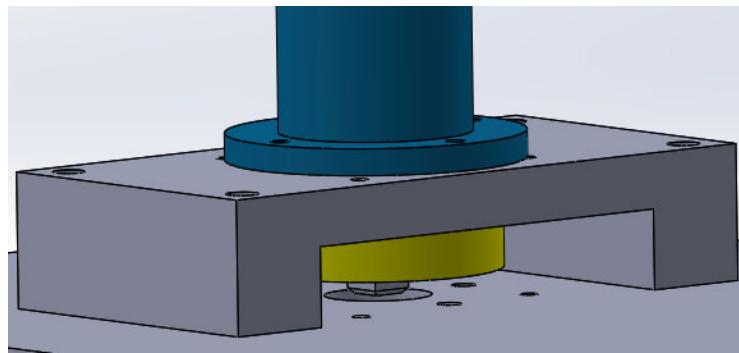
Disposition de l'amortisseur (jaune) sur le nouvel assemblage de l'axe de rotation J1. La pièce bleue est la cage de roulements.
